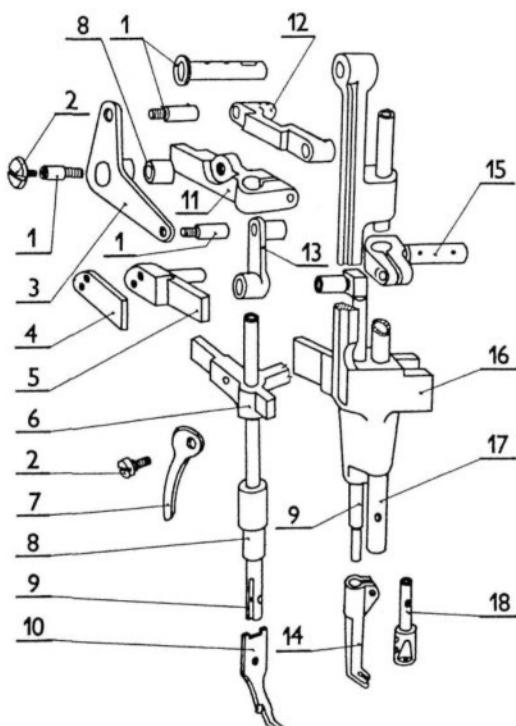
Podávací ústrojí zvláštní [7]
